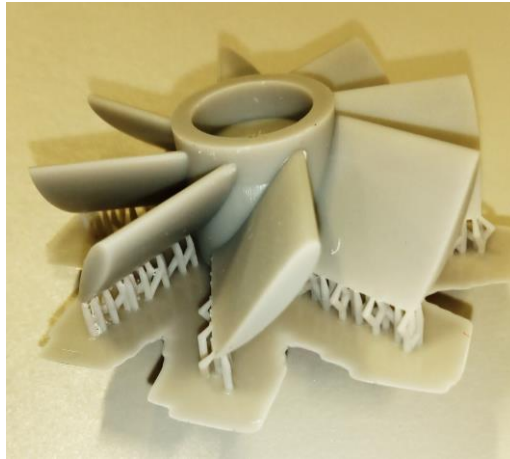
Hélice con ángulo de ataque de 45° impresa con la impresora de resinas
